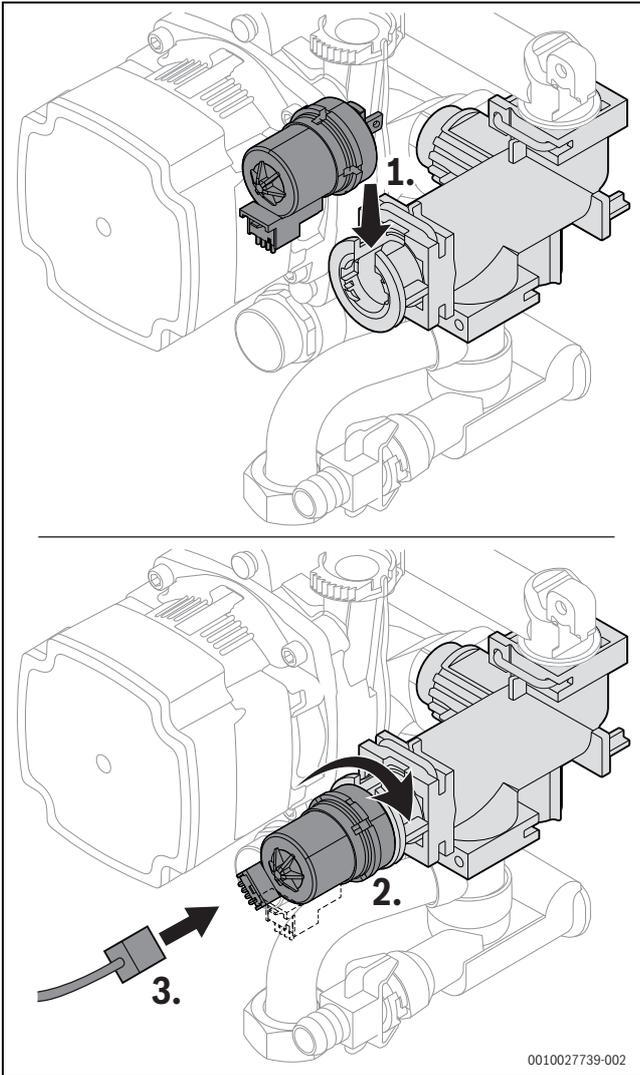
Motor am 3-Wege-Ventil einbauen (Variante ohne Schrauben)
